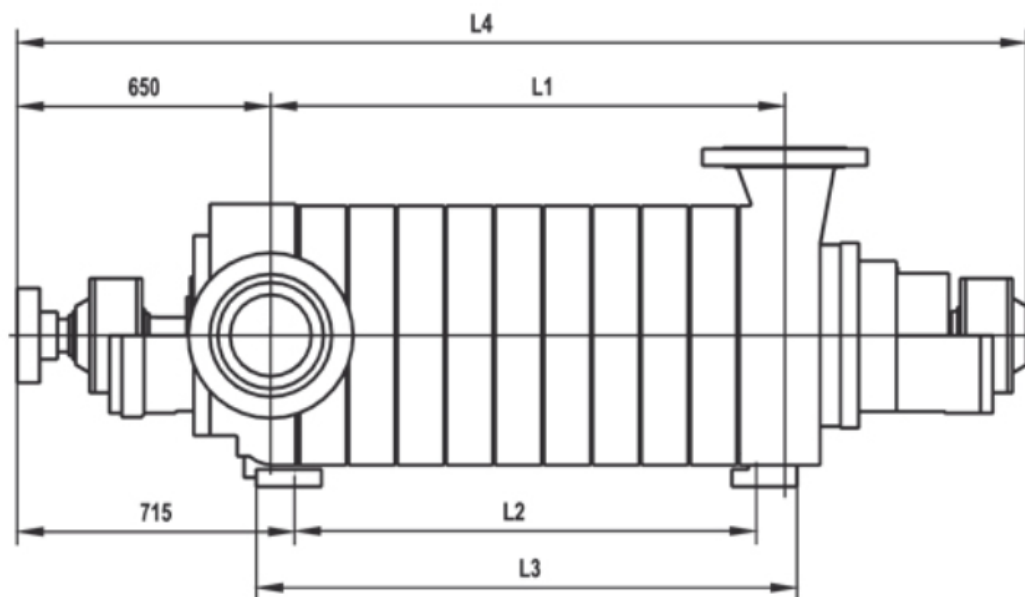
Габаритные размеры ЦНСн 315-126
